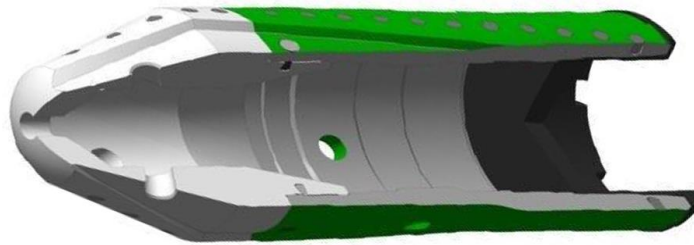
Башмак прорабатываемый с вооруженной насадкой БКПВН
